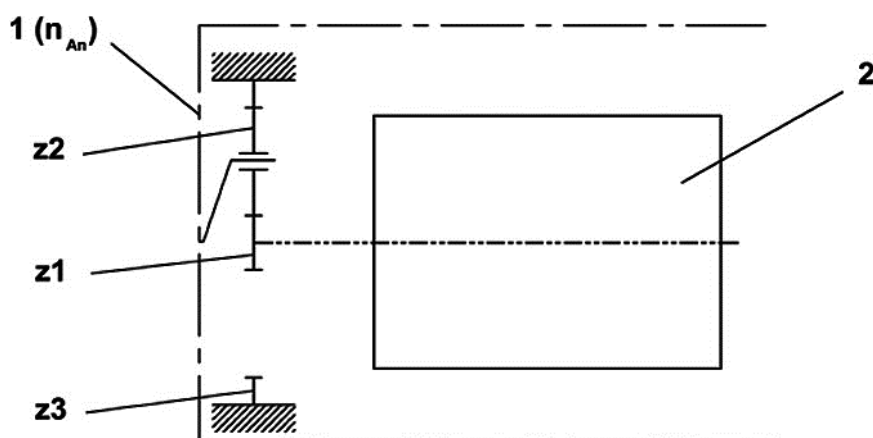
Кинематическая схема поворотного редуктора дробилки:
